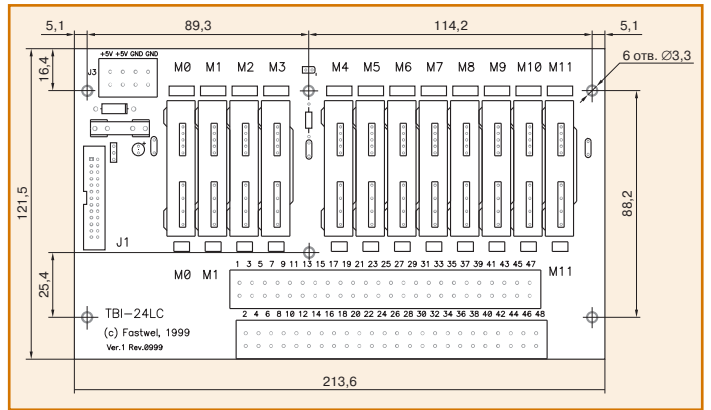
Габаритный чертеж панели TBI-24LC фирмы Fastwel
